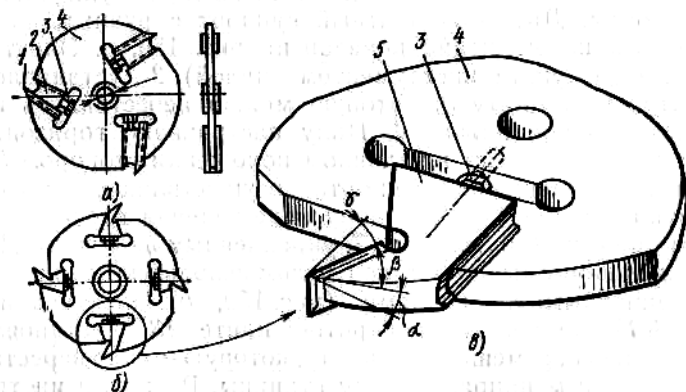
Фрезы дисковые пазовые для обработки проушин: а — крепление резца клином, б, в — распорным винтом; 1 — резец, 2 — клин, 3 — винт, 4 — диск, 5 — резец-клин
